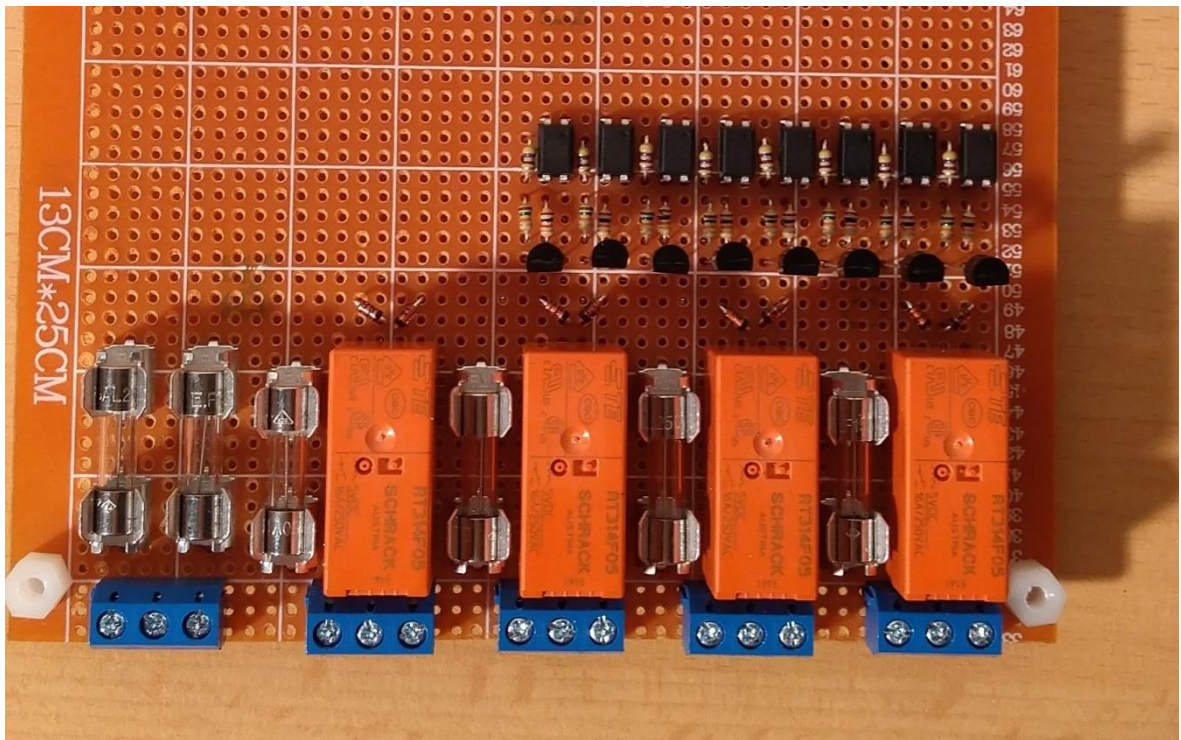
Zdjęcie przedstawiające gniazdo zasilające wraz z gniazdami wyjść, przekaźnikami zabezpieczonych bezpiecznikami
